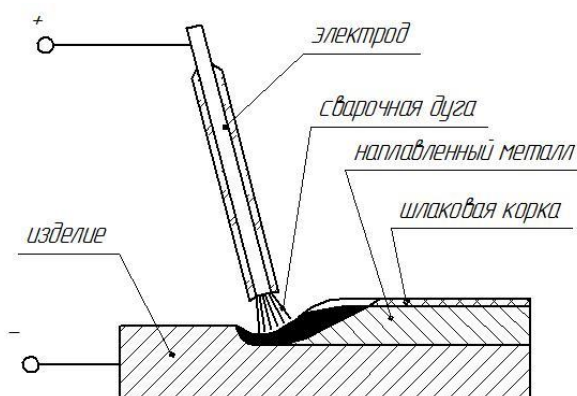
Схема осуществления ручной электродуговой сварки штучными электродами
